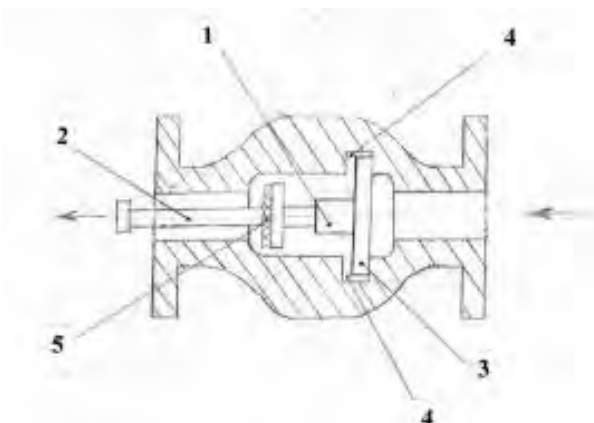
Конструкционная схема гидроударного насоса в разрезе (вид сверху):
